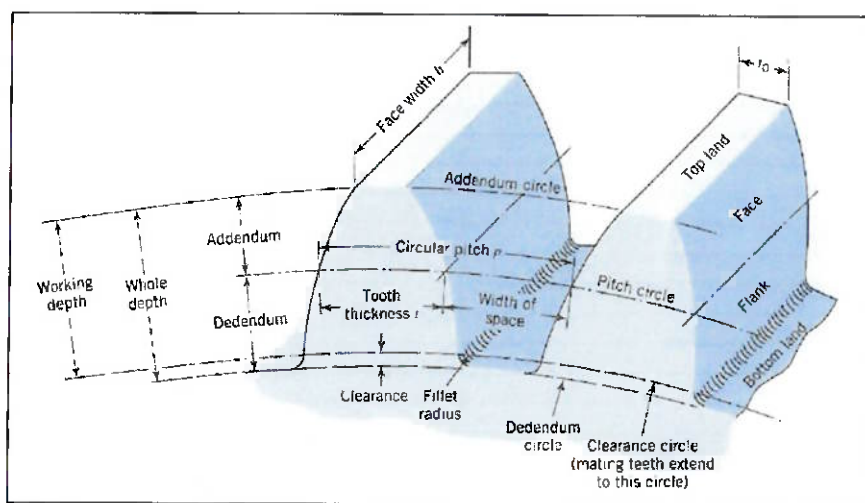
Dimensões e nomenclatura de uma engrenagem
